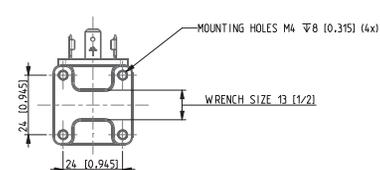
Dimensioni 1/8" in linea, larghezza bobina 32
